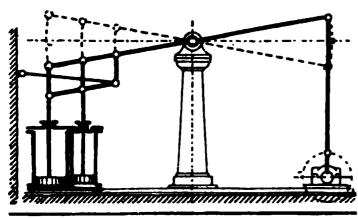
Woolfsche Balanciermaschine mit gleichgerichtetem Kolbenlauf, wird noch jetzt für Pumpmaschinen etc. ausgeführt.
